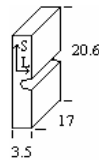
Eprouvette entaillée TL, dimensions en mm
